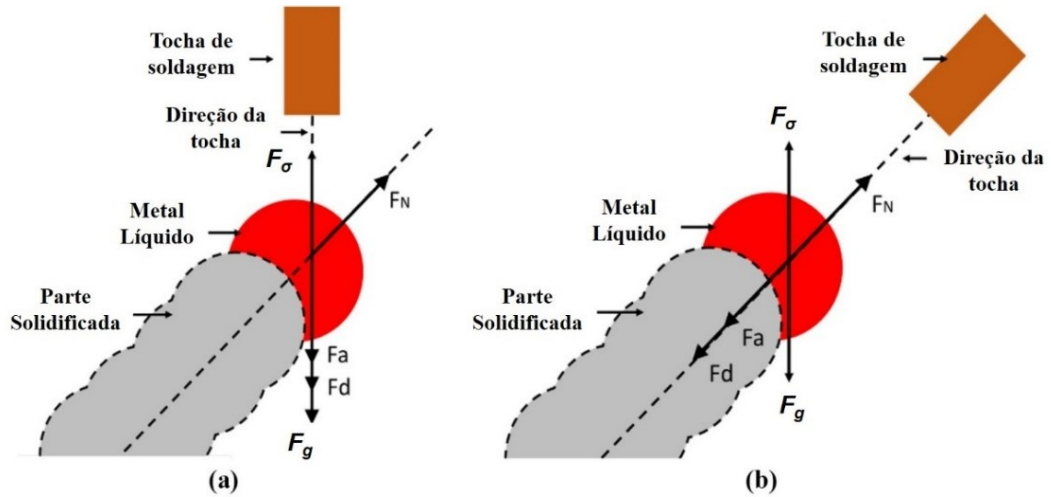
Tocha de soldagem (a) perpendicular e (b) inclinada em relação ao substrato (adaptada pelo autor)
